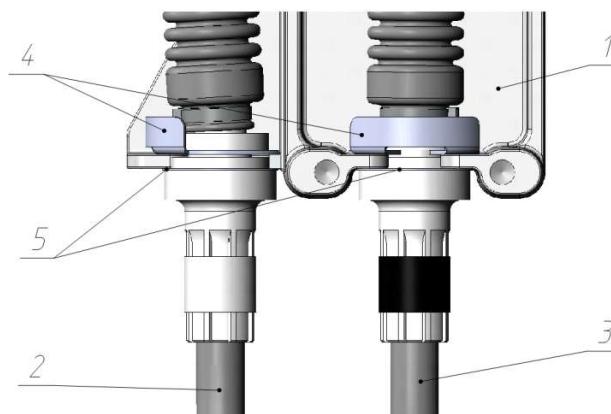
Установка тросов в корпусе мастер-опоры
